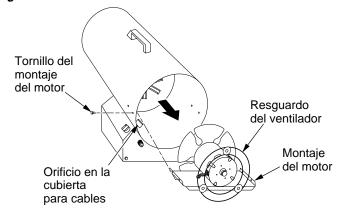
Desmontaje del motor, del montaje del motor y del resguardo del ventilador del calentador
